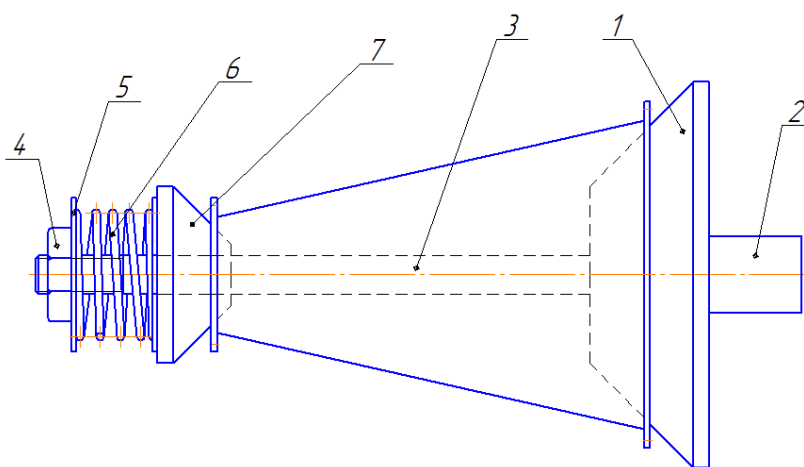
Спеціальний складально-притискний пристрій
